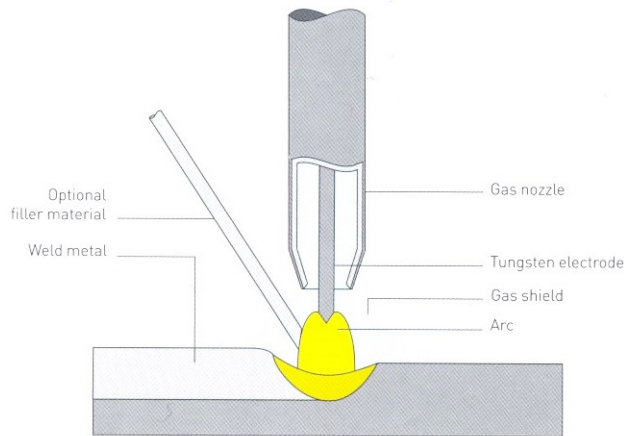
Esquema soldadura TIG, Fuente: Manufacturing processes for design professionals, Autor: Rob Thompson (Thompson, 2007)
